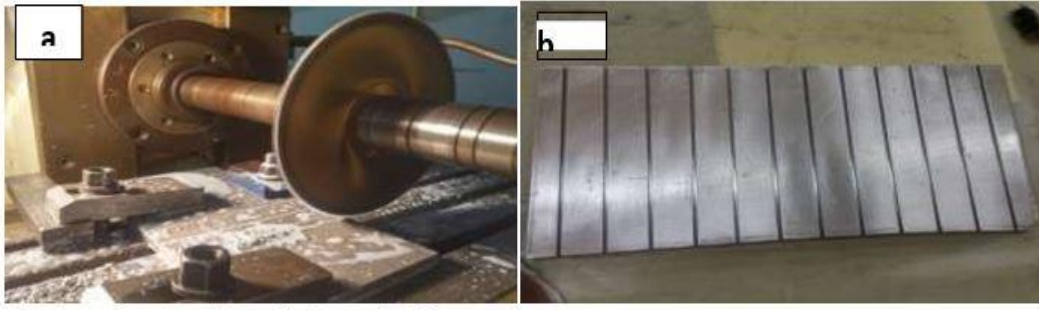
a) Fraiseuse horizontale automatique d'usinage (l'usinage de la tôle) .b) la tôle après l'usinage des rainures
